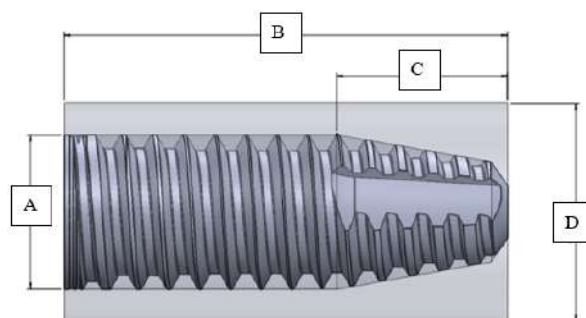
Implante dentário com dimensões básicas a serem usinadas (Autor)
